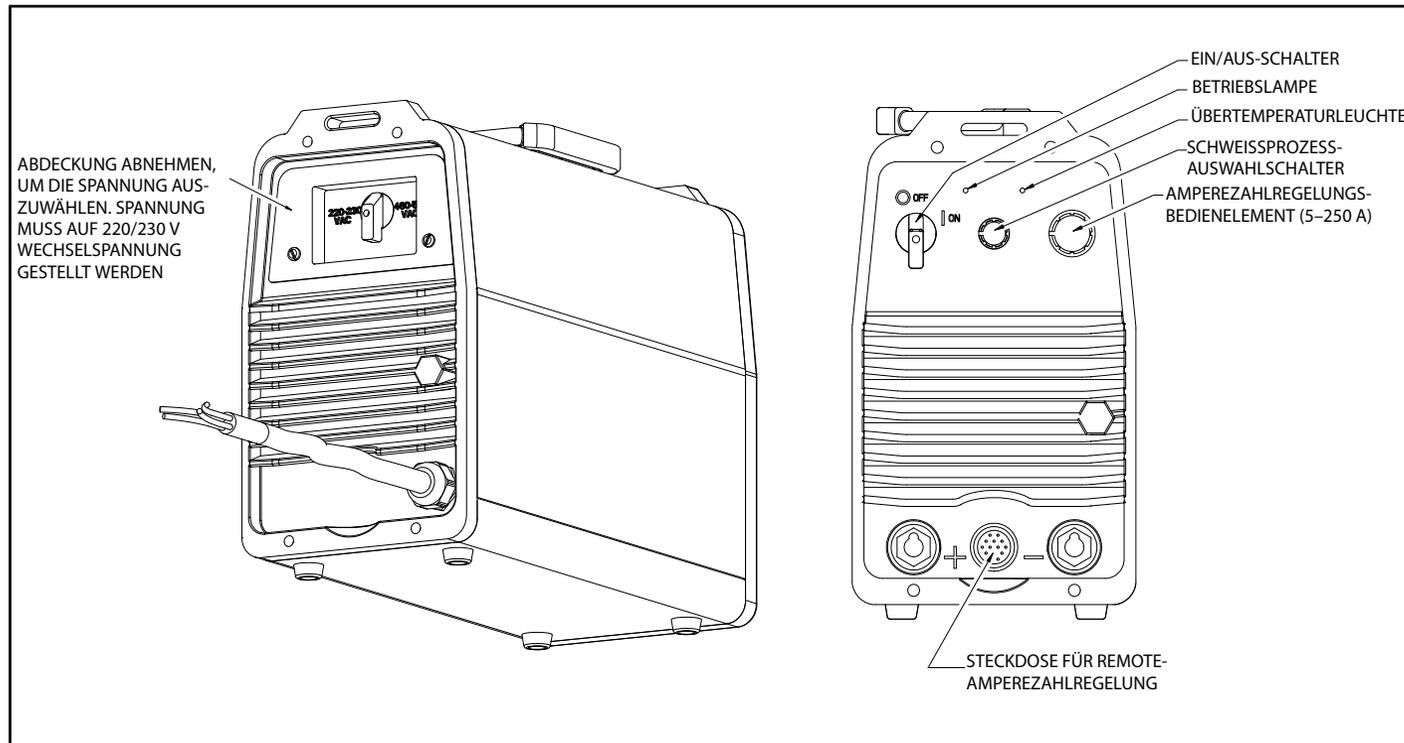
SkyWelder™ – Blatt 2 von 2
